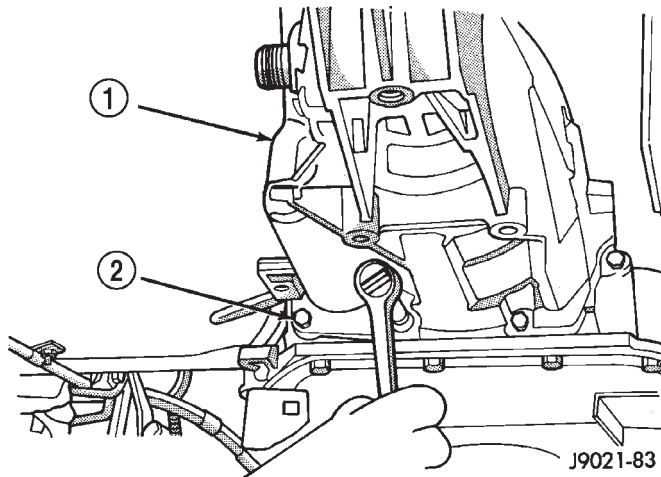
Befestigungsschrauben der Overdrive-Einheit
